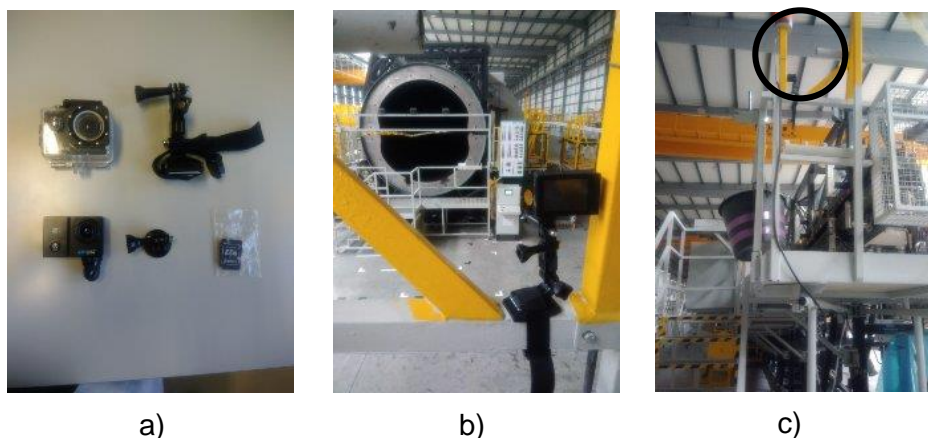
Ferramentas de filmagem e posição no molde – a) máquina de filmar; b) posição 1; c) posição 2
